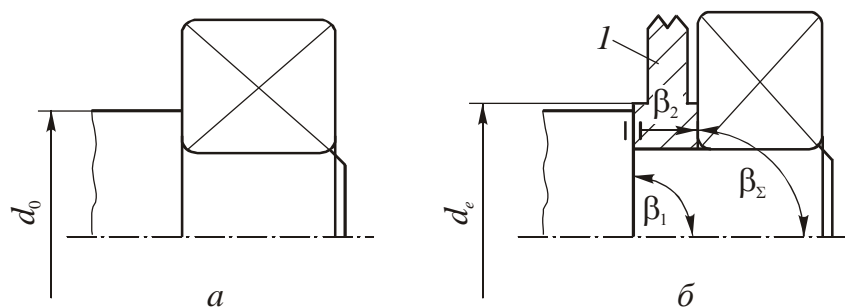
Варианты конструкции подшипниковых опор вала
